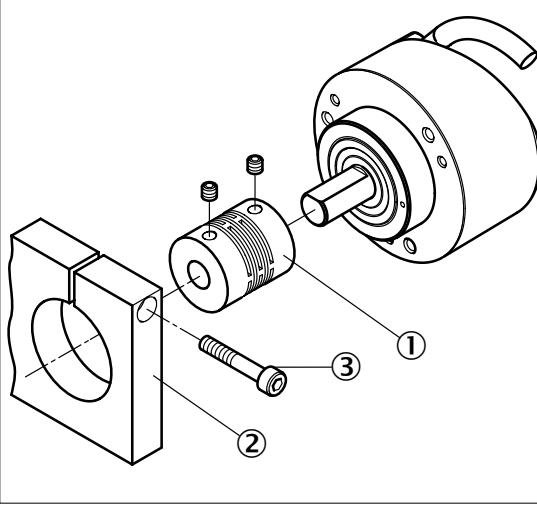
Anbau Servoflansch über flanschseitige Gewindebohrungen
